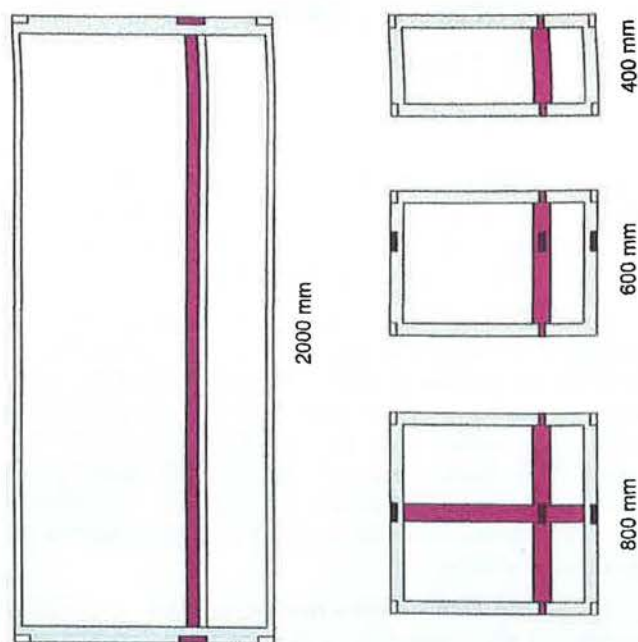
Planta de armazón con subconjuntos de distintos soportes.
